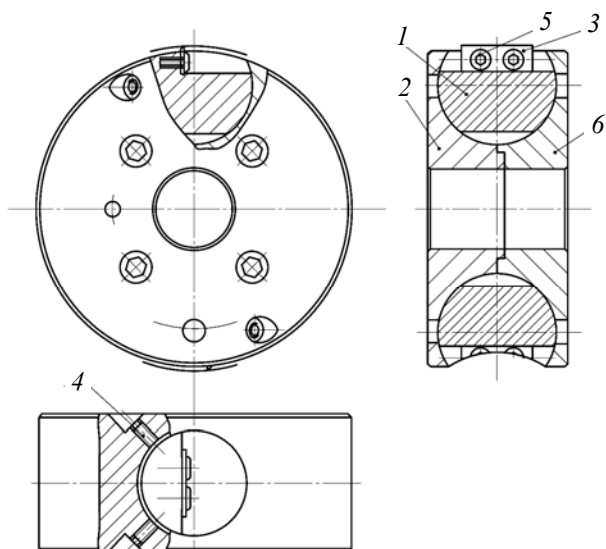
Фреза сборная с адаптивными свойствами (изменяемыми углами)
